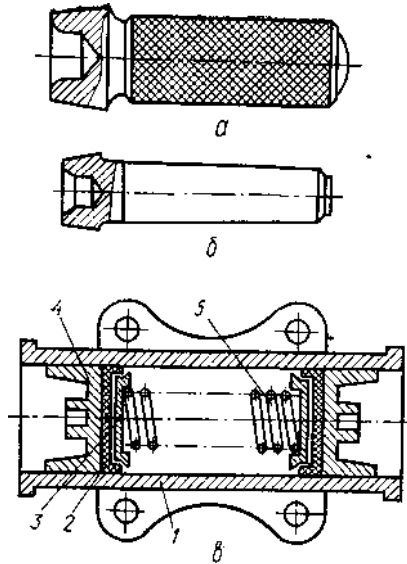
Пристрій для ремонту і схема складеного гальмового циліндра:
